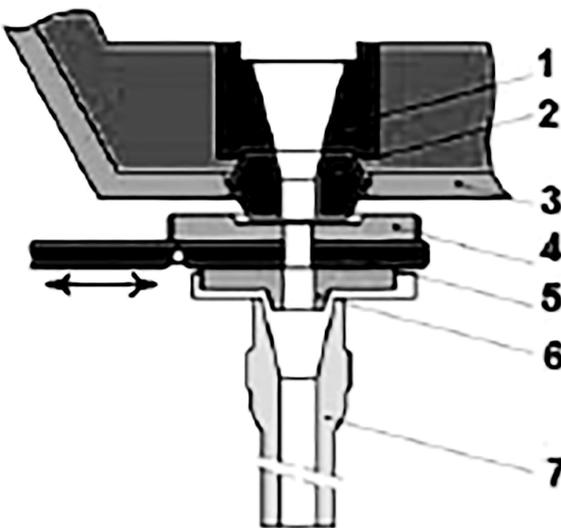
Схема подачи металла из промковша через трехплитный шиберный затвор [4]
